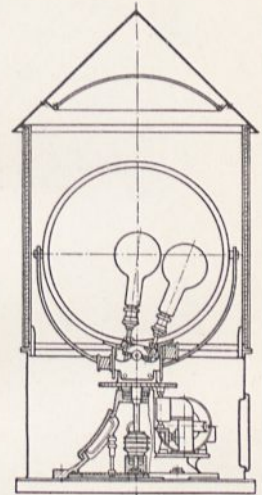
Schnitt durch das Drehfeuer Type DF mit automatischer Glühlampenaustauschvorrichtung.
